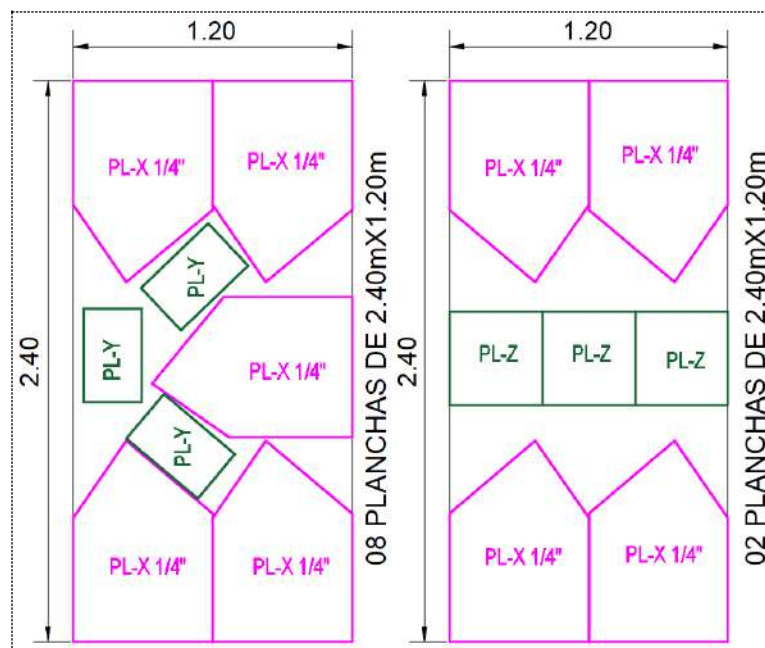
Detalle ubicación de Cajuela de apoyo y plancha PL-Y y PL-Z
